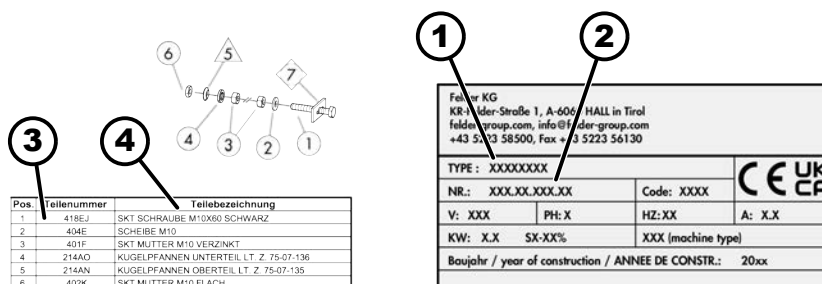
Liste des pièces de rechange / plaque signalétique
